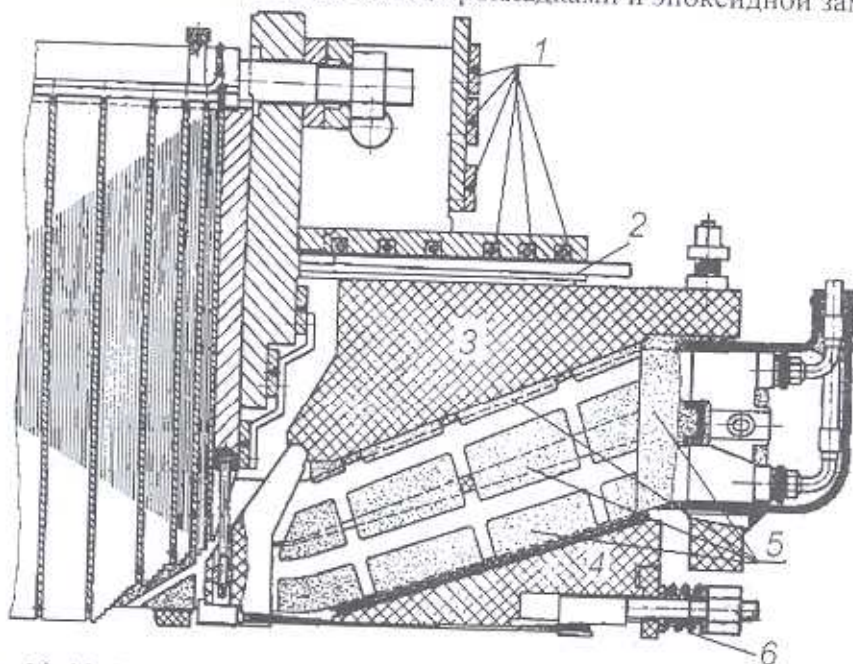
Крепление лобовых частей обмотки статора ТЗВ-800-2:
